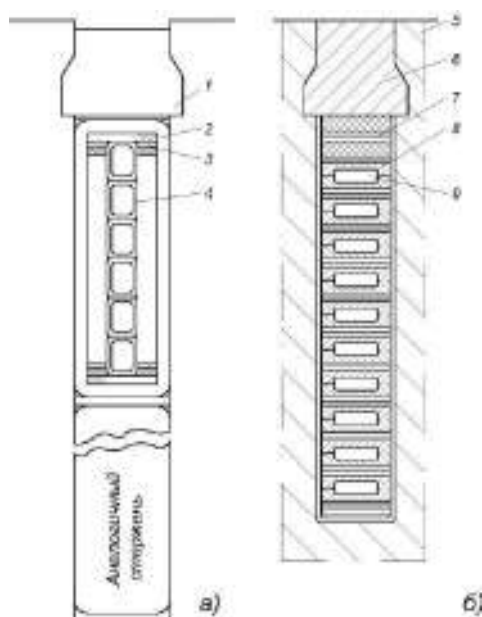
Разрез паза статора а) и ротора б) генератора типа ТГВ: 1 – пазовый клин; 2 – корпусная изоляция ; 3 – массивный элементарный проводник; 4 – газовые трубки; 5 – бочка ротора; 6 – дюралюминиевый клин; 7 – подклиновка изоляция; 8 – полувитки обмотки; 9 – горизонтальный вентиляционный канал
